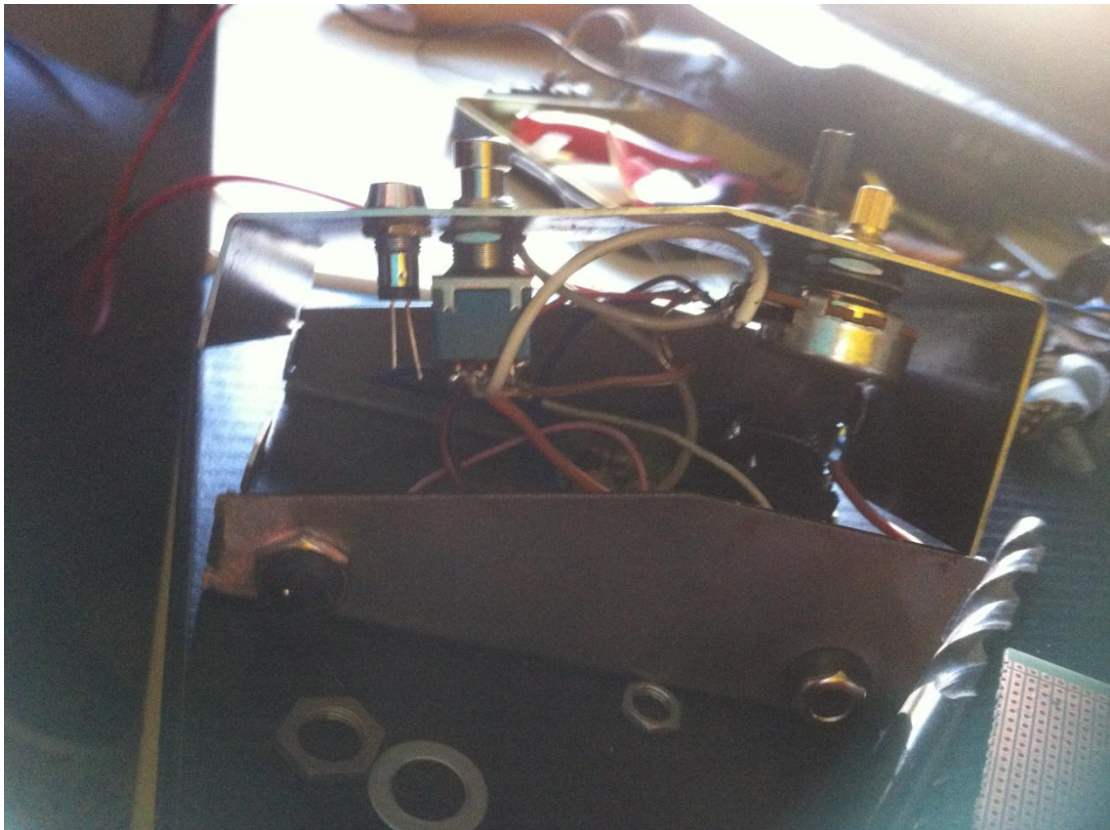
Πειραματικό στάδιο, Δημιουργία κυκλώματος EM Drive σε PCB πλακέτα
